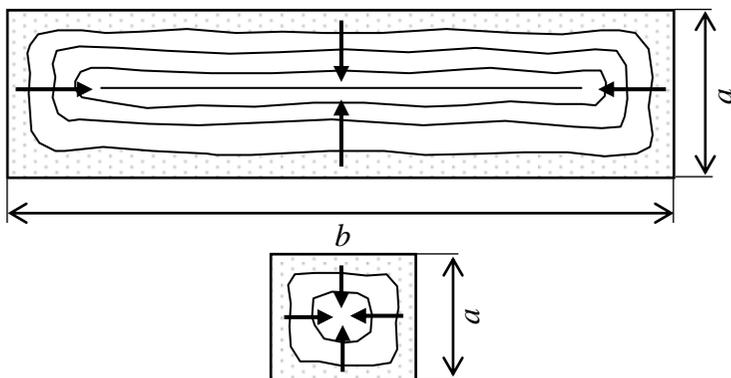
Схематичное изображение продвижения фронта кристаллизации в поперечном сечении слябовой (вверху) и сортовой (внизу) непрерывнолитых заготовок:  $a$  – толщина;  $b$  – ширина заготовки
